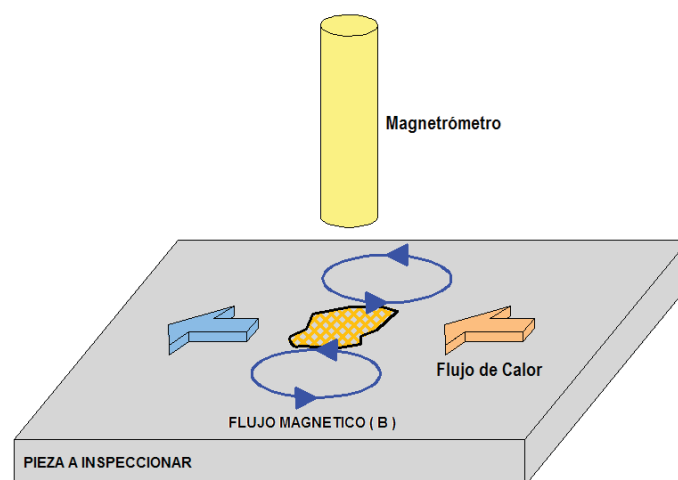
5.- Esquema de la técnica de termoelectricidad de no contacto.
